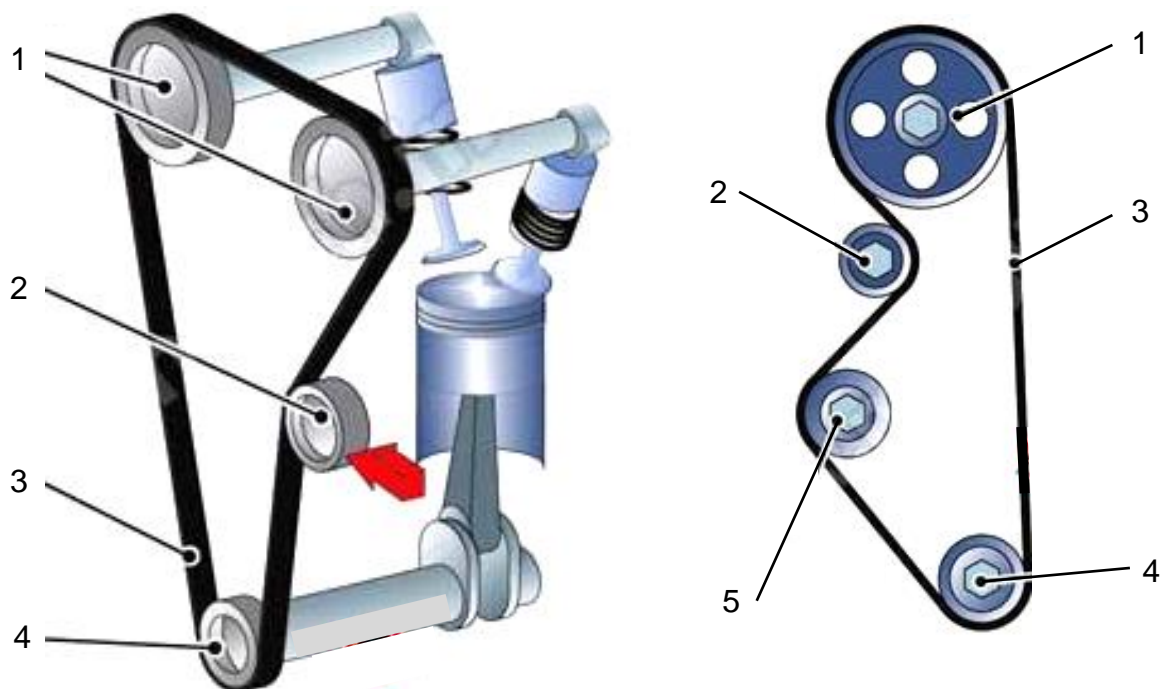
Схема ремінного приводу газорозподільного механізму: 1 – шків розподільного вала; 2 – ролик натягувача реміня; 3 – ремінь приводу; 4 – шків колінчастого вала; 5 – проміжний ролик
